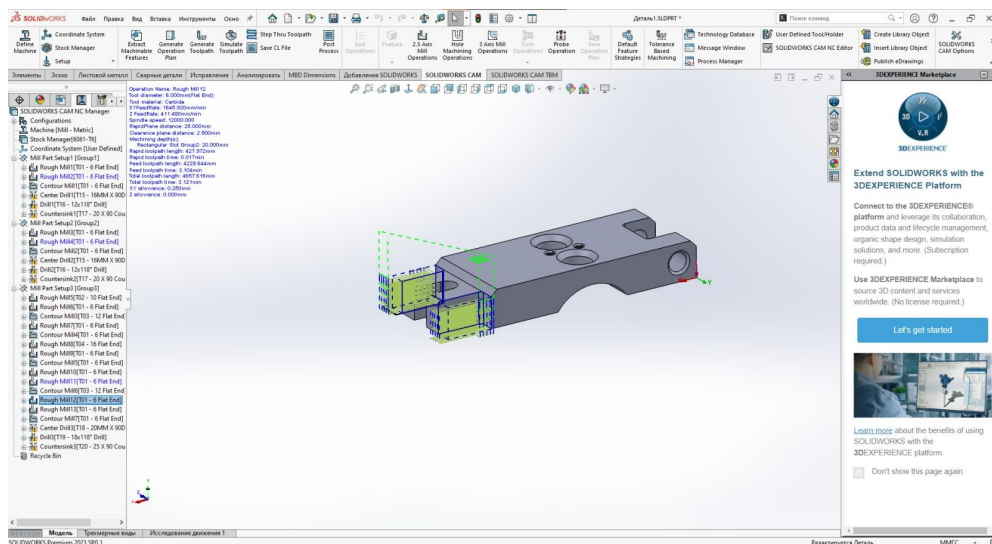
Траекторія обробки - фрезерування бокової поверхні
